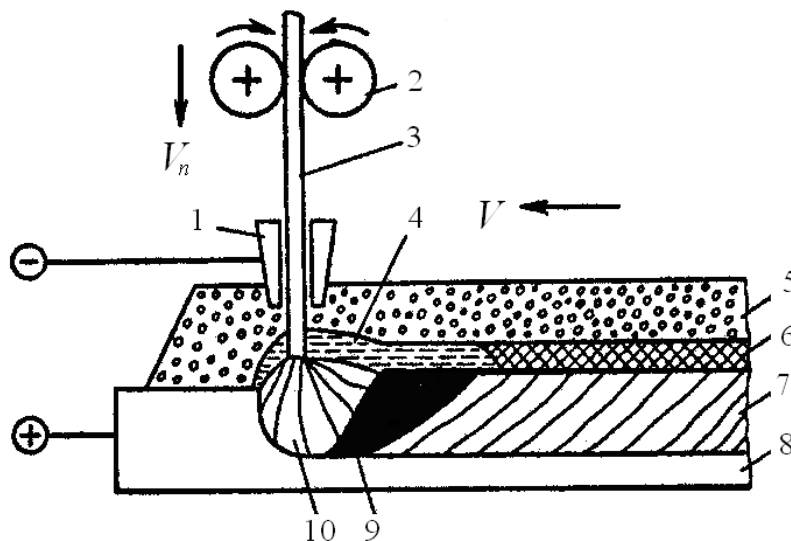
Схема автоматичного дугового зварювання під флюсом: 1 – струмопровід; 2 – механізм подачі електродного дроту; 3 – електродний дріт; 4 – ванна рідкого шлаку; 5 – флюс; 6 – шлакова кірка; 7 – зварний шов; 8 – основний метал; 9 – ванна рідкого металу; 10 – зварювальна дуга
